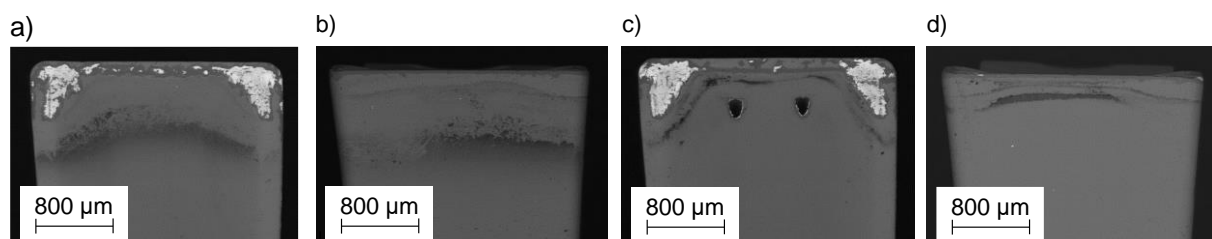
Werkzeugschneiden nach Erreichen des Abbruchkriteriums bei der Bearbeitung von X6CrNiMoTi17-12-2; a) Spanfläche des Referenzwerkzeuges, b) Freifläche des Referenzwerkzeuges; c) Spanfläche des microCutOff-Werkzeuges, d) Freifläche des Referenzwerkzeuges
